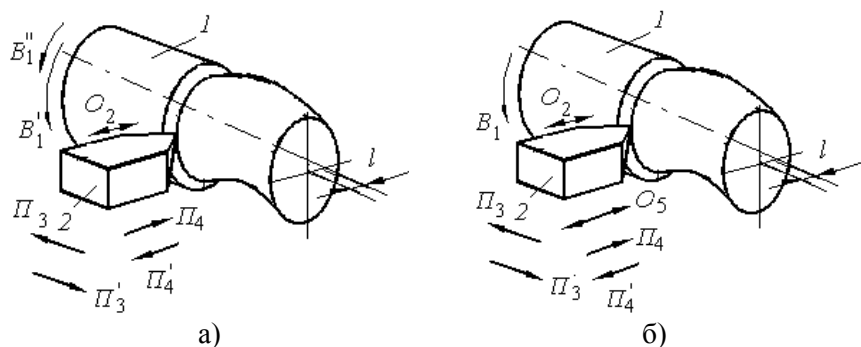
Схемы точения КВП при сообщении дополнительного движения заготовке (а) или резцу (б)
